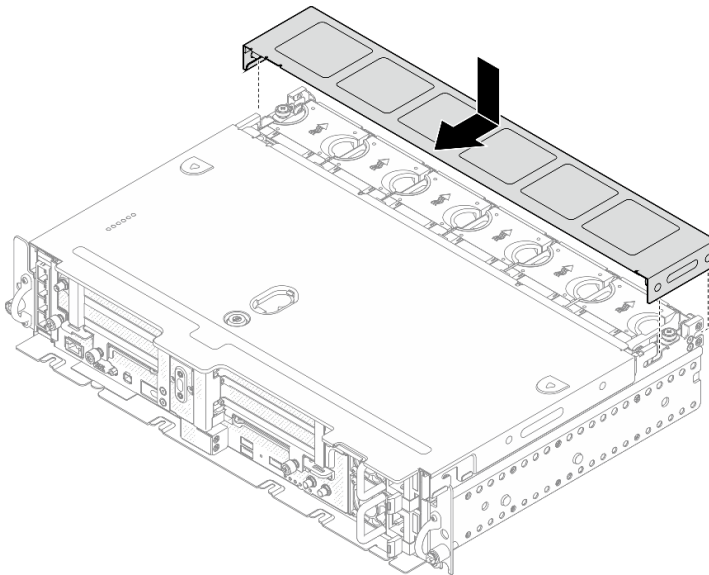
Instalación de la cubierta del ventilador (300 mm)
